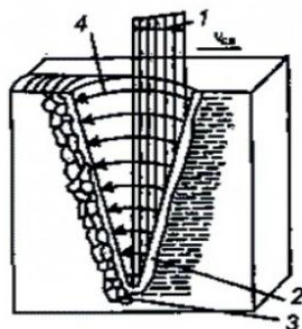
Форма проплавления по технике лучевой сварки:
